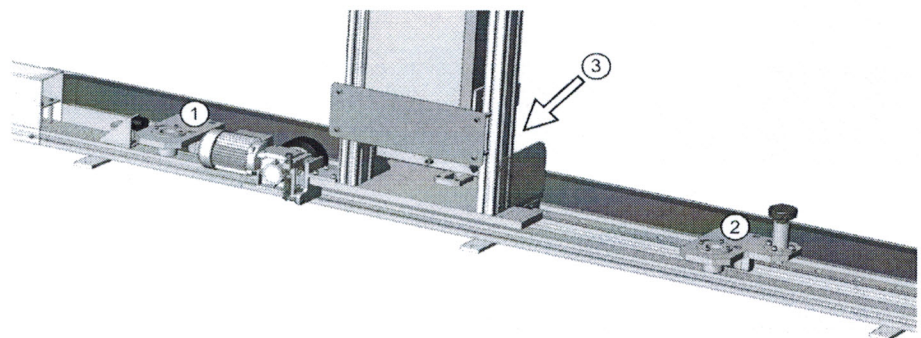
Приспособление калибровочное Single Axle Master Gauge, установленное на стенде для измерений углов установки колес автомобилей модели x-wheel truck d.
